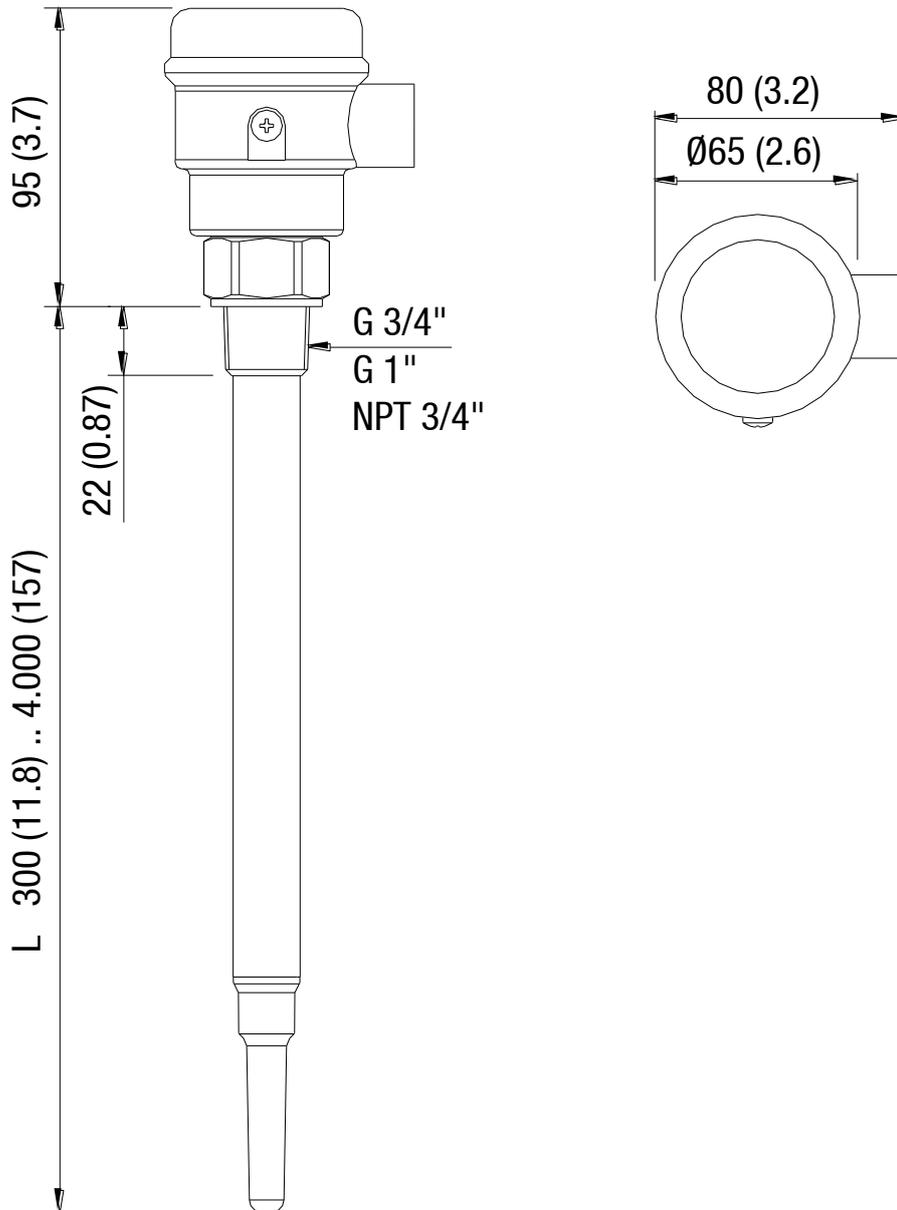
Abmessungen CN 7130, Gehäuse Ø 65 mm
